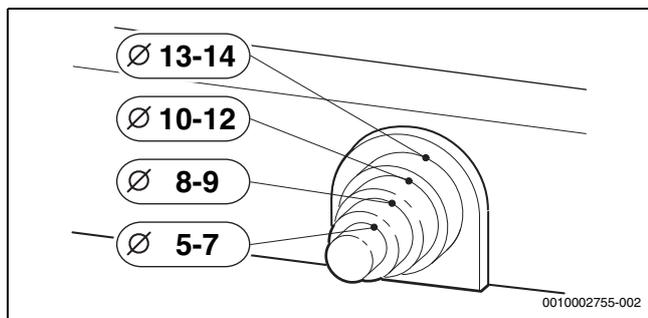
Zugentlastung Kabel Mischermotor anpassen
